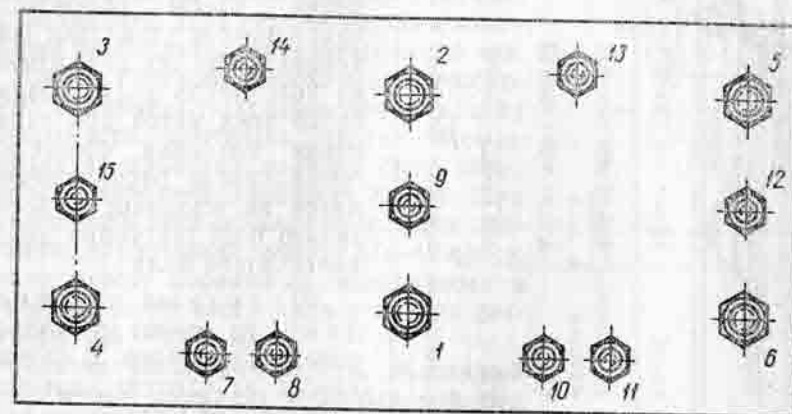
Схема затяжки гаек шпилек крепления головки цилиндров (1, 2, 3 ... 15 — цифры, обозначающие порядок затяжки)
